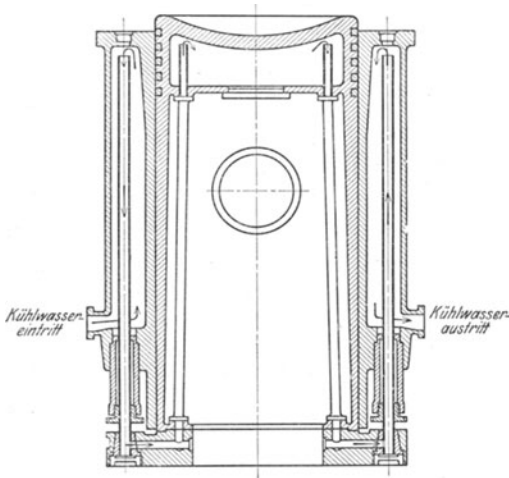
Tauchkolben einer Zweitaktmaschine.
